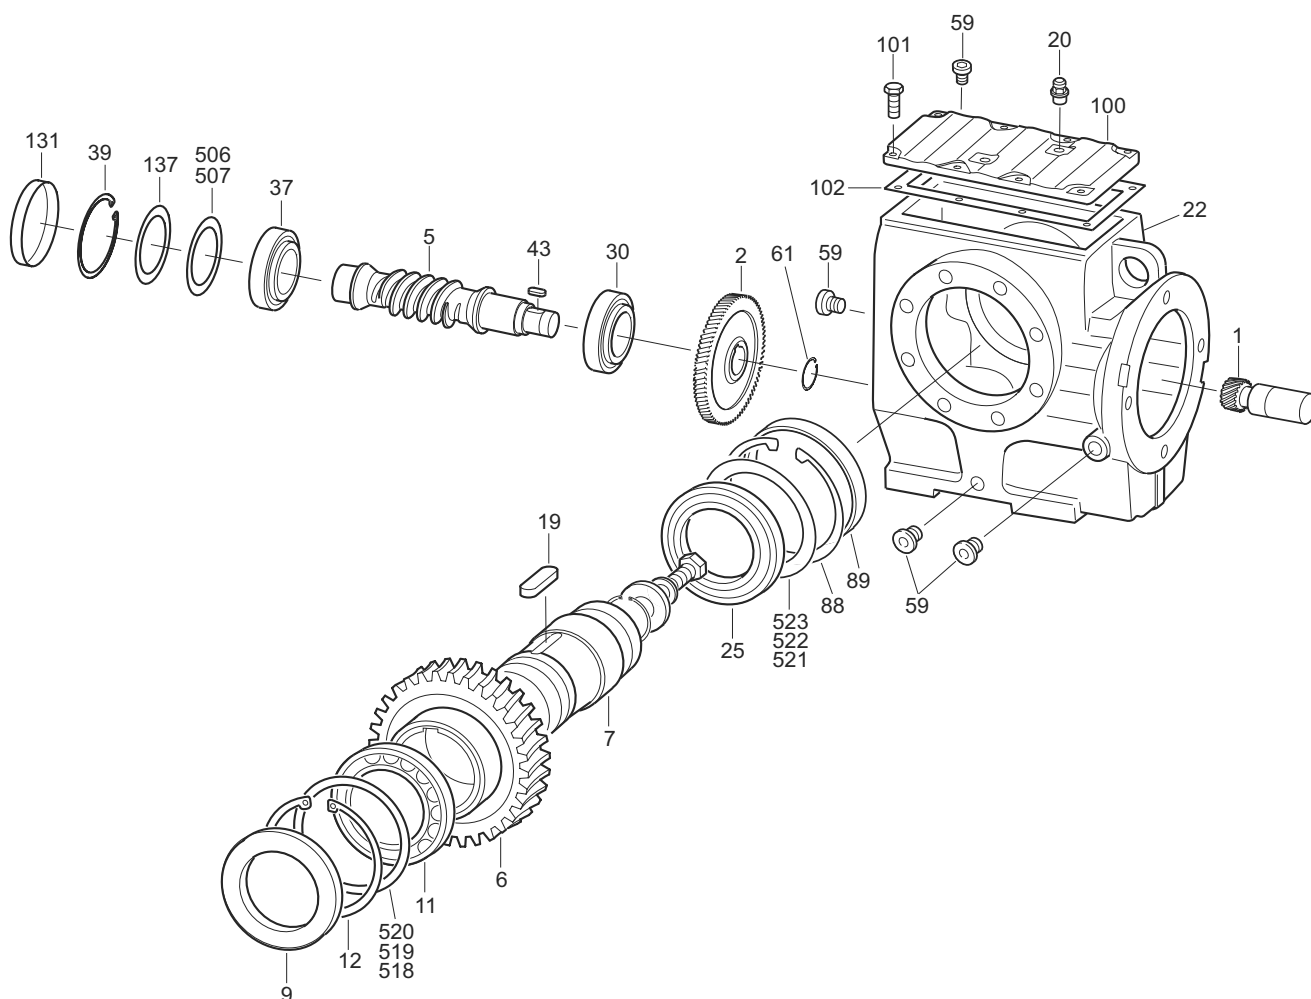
Estrutura geral do redutor de engrenagens cônicas
